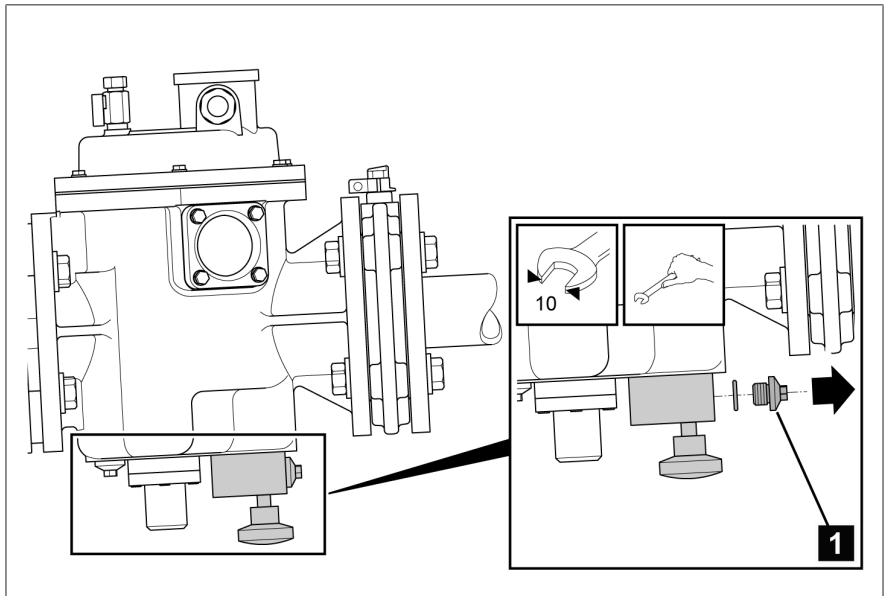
Schraube im Block am Geräteboden entfernen (Beispiel am Bypass BPM)
